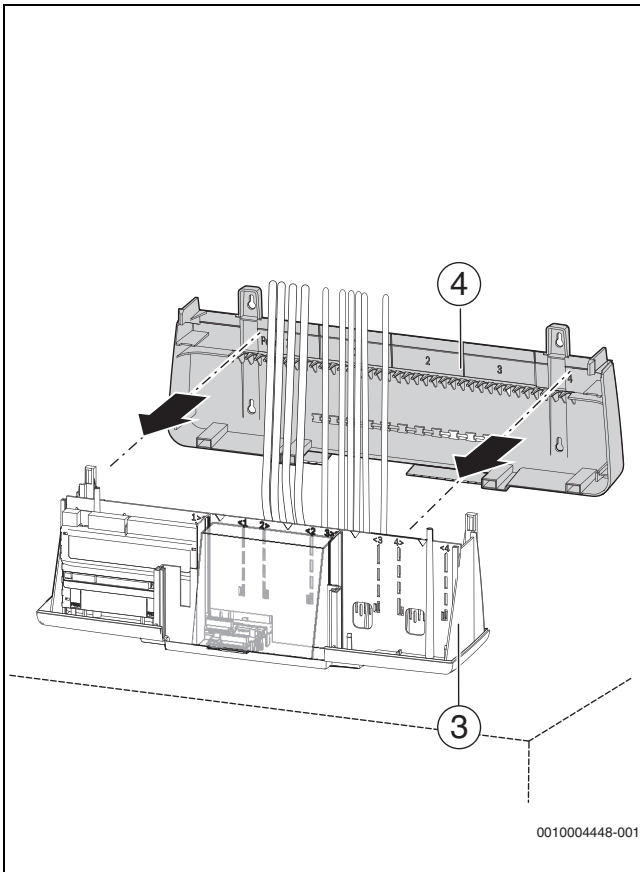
Montage auf Kessel, aufstecken Rückwand einrasten
